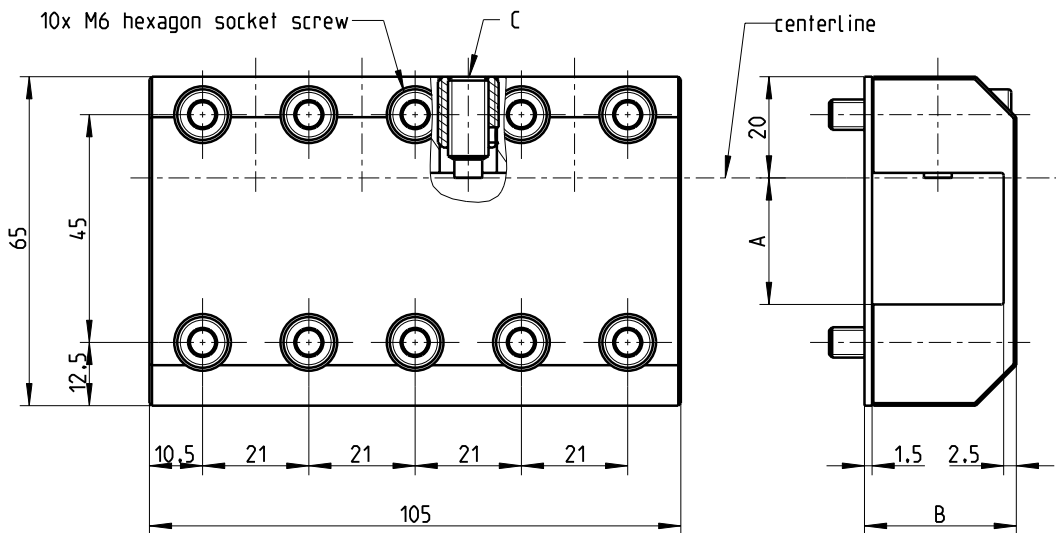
Werkzeughalter für Drehmeißel für axial montiertes Dynamometer, Typ 9129AE...
